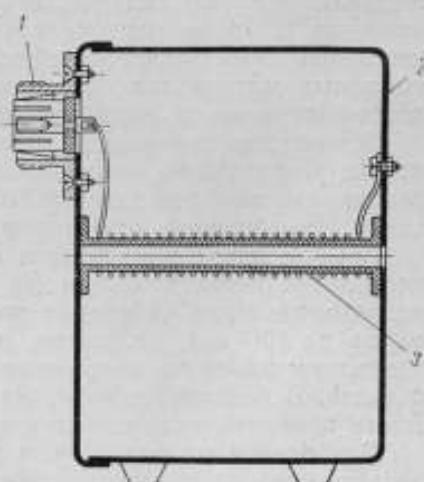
Конструкция измерителя напряженности магнитного поля. 1 — средний разъем; 2 — корпус-экран; 3 — соленоид.
